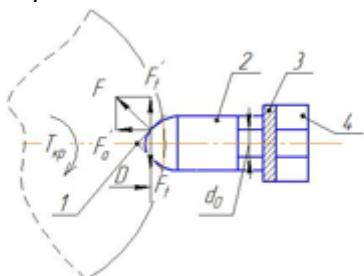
Схема сил, які діють на плунжер та пластину: 1 – вставка; 2 – плунжер; 3 – пластина; 4 – втулка; 5 – корпус
